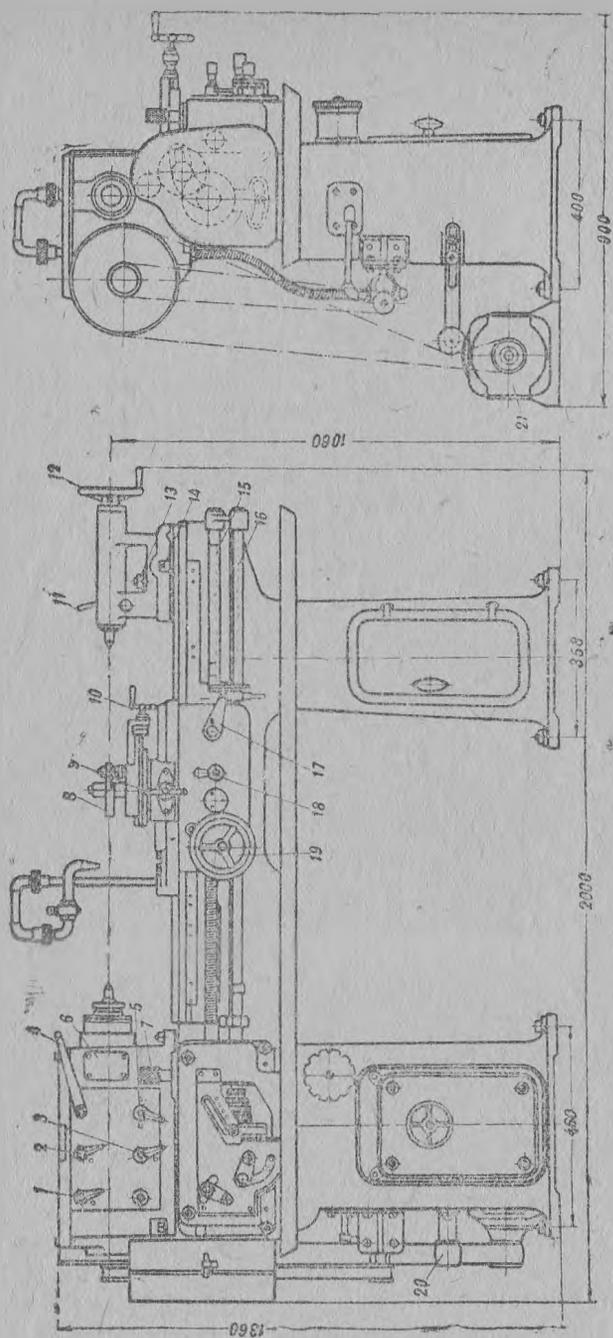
Токарно-винторезный станок СЛ-162 (вид спереди и сбоку).
